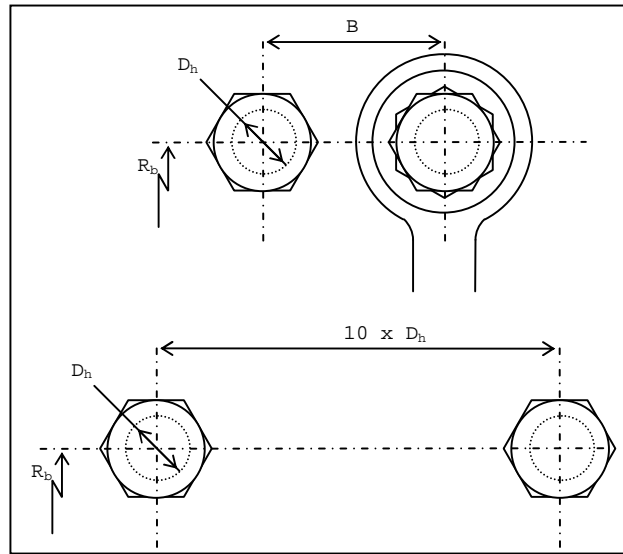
Dimensiones de Herramental de 12 puntos de Agarre
